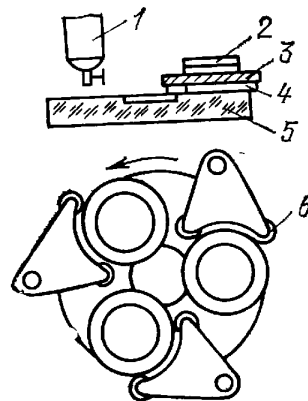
Схема плоскошлифовального станка и расположение головок:
